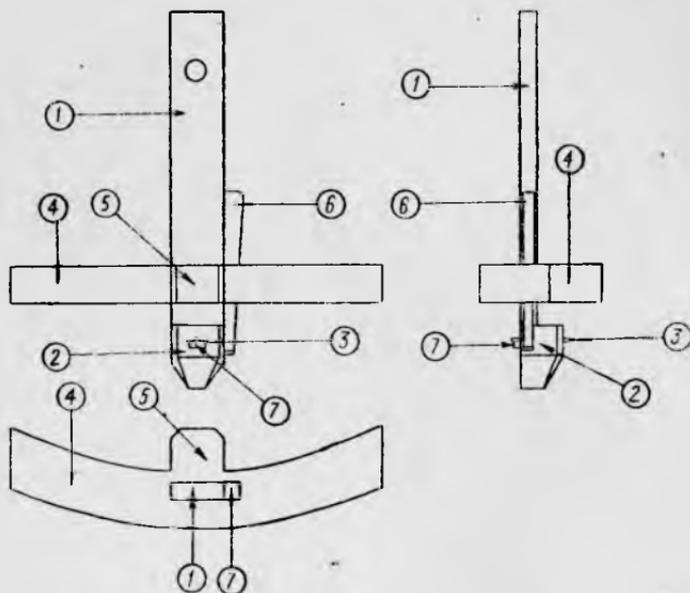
«Гребень»: 1—планка с головкой, 2—головка, 3—резцы, 4—колодка, 5—опорный выступ, 6—клин для закрепления планки, 7—клин для закрепления железки
